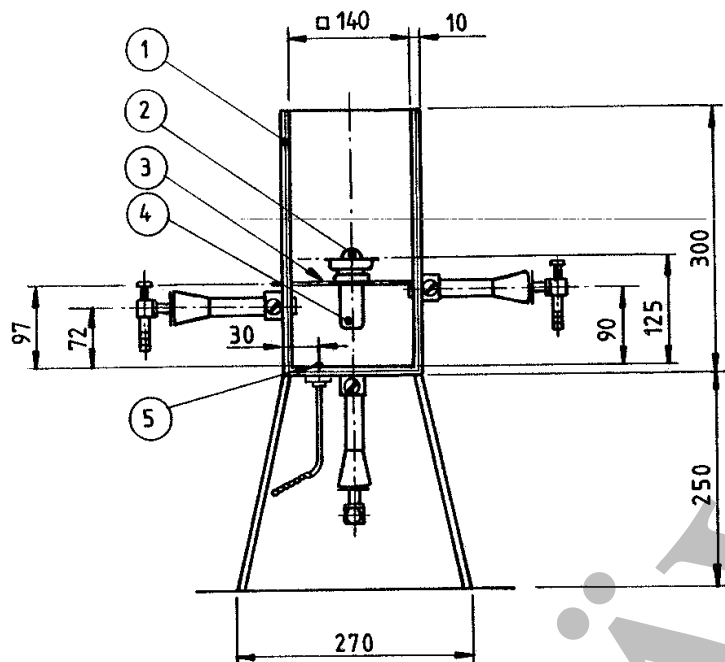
2 EXPLOSIONSSÄKERT HÖLJE MED GASBRÄNNARE FÖR UPPVÄRMNING AV STÅLHYLSA MED UTBLÅSNINGSHÅL
